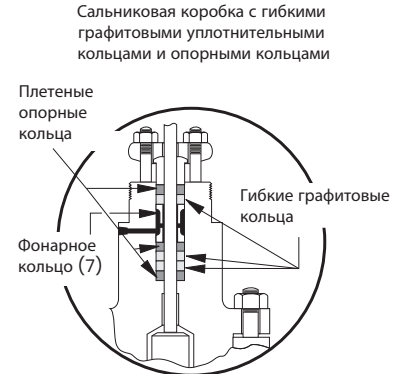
Компоновка уплотнительных колец в крышке с дополнительным соединением для смазочного устройства
